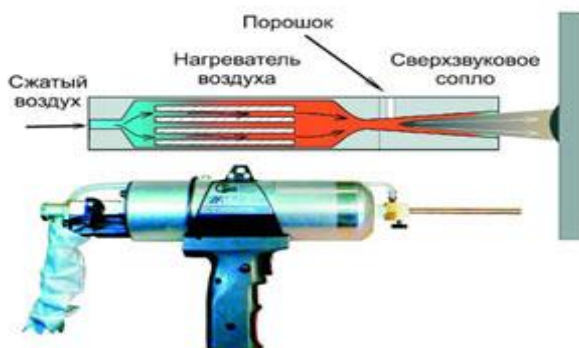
Схема сверхзвукового аппарата для напыления металлических покрытий (сверху); общий вид аппарата (снизу)
